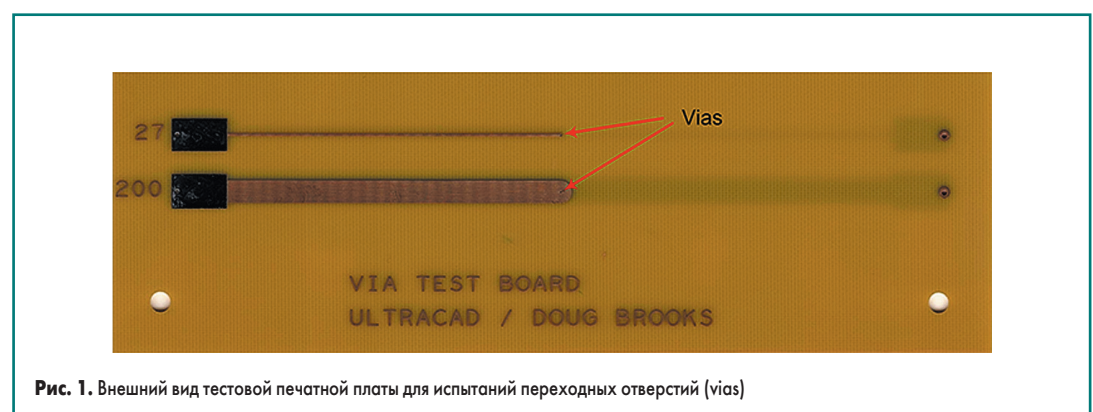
Внешний вид тестовой печатной платы для испытаний переходных отверстий (vias)
